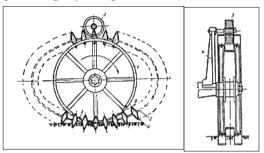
Зацепление выступов гусеницы (полученных путем штампования) с отверстиями колеса
